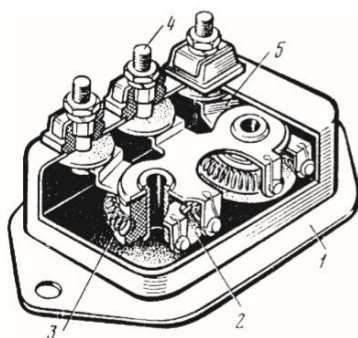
Добавочный резистор СЭ107: 1 – корпус; 2 – фарфоровый изолятор; 3 – спираль резистора; 4 – вывод; 5 – пластина
